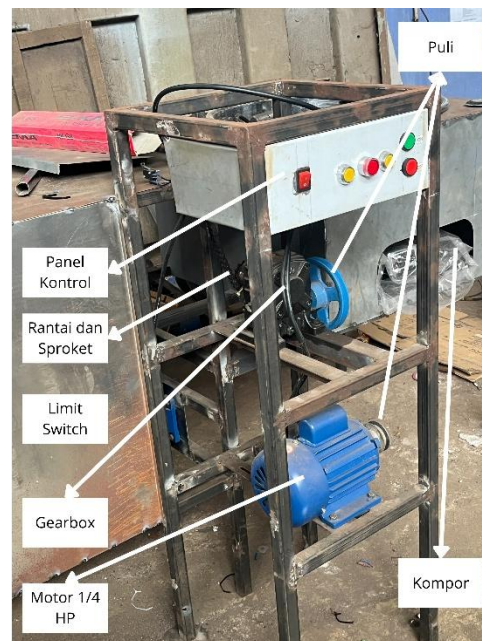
26 Pemasangan Motor, Puli, Sabuk, *Gearbox* dan Rantai Penggerak Tuas
